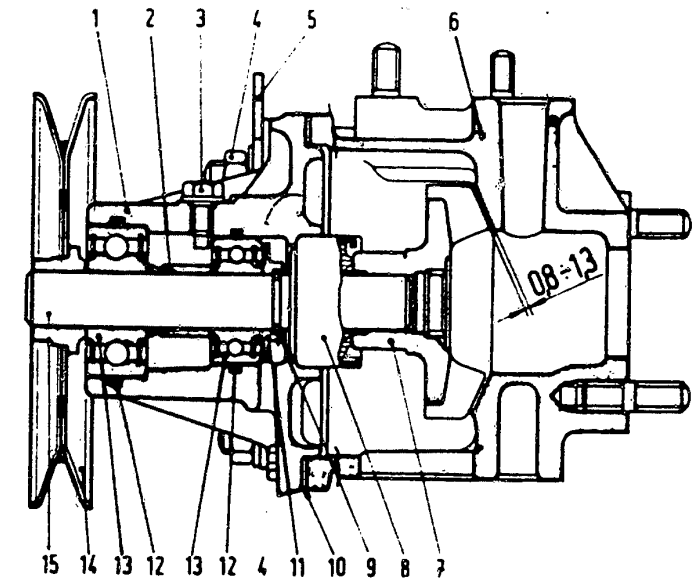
1116- und 1301-cm³-Motor: Das Spiel zwischen dem Wasserpumpenrad und dem Gehäuse soll 0,8 ... 1,3mm betragen. Es bedeuten ferner: 1 Pumpendeckel – 2 Distanzbuchse – 3 Schraube – 4 Befestigungsmuttern für Pumpengehäuse – 5 Haltebügel – 6 Pumpengehäuse – 7 Pumpenrad – 8 Dichtring – 9 Sicherungsring – 10 Flachdichtung – 11 Anlaufscheibe – 12 Dichtring – 13 Kugellager – 14 Keilriemenscheibe – 15 Pumpenwelle.
